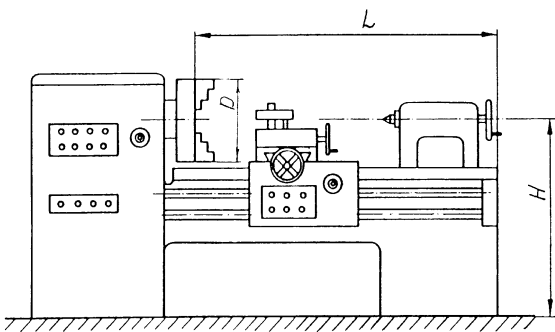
Die Hauptabmessungen einer Drehmaschine /2/; D-Durchmesser, L-Länge, H-Höhe
